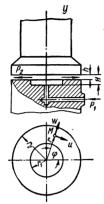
Гидростатический упорный подшипник с центральной камерой
